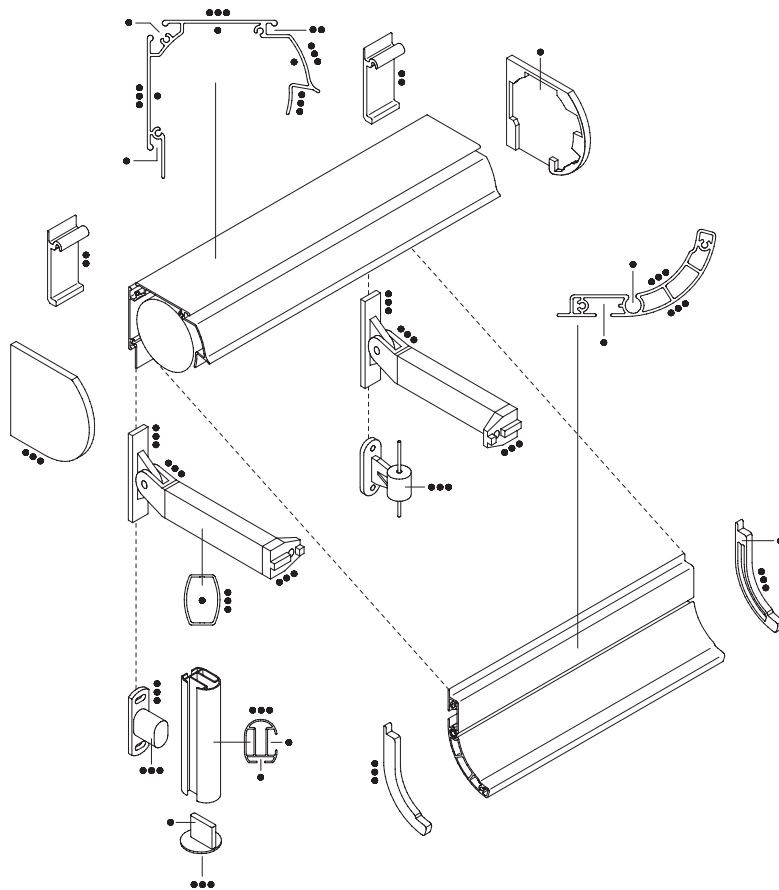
Sichtflächendefinition - Fassadenmarkisen
